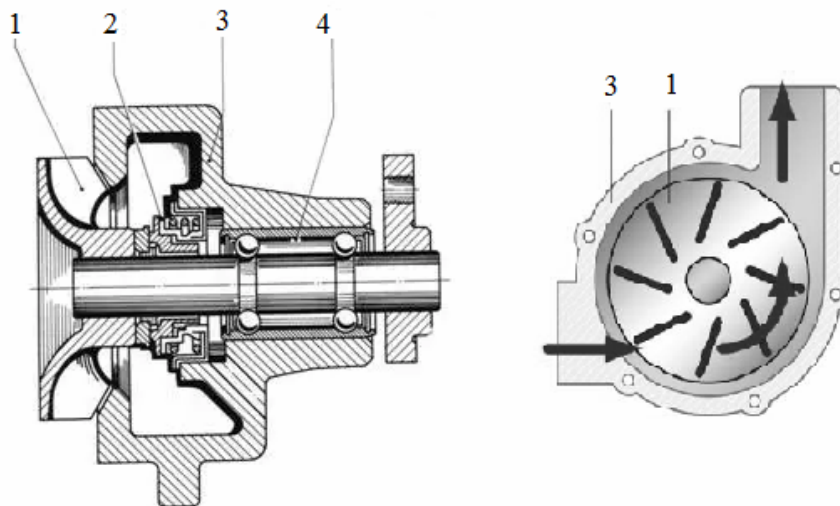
Pompa de lichid: 1- rotor cu palete; 2- presetupă; 3- corp pompă; 4- rulment
